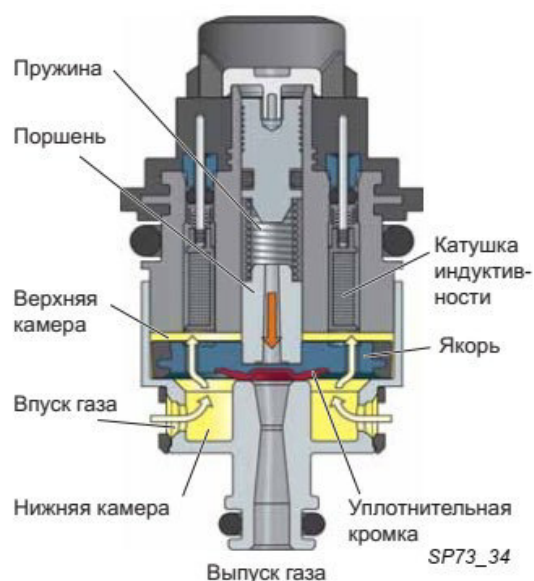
Схема роботи газової форсунки (закритий стан)
